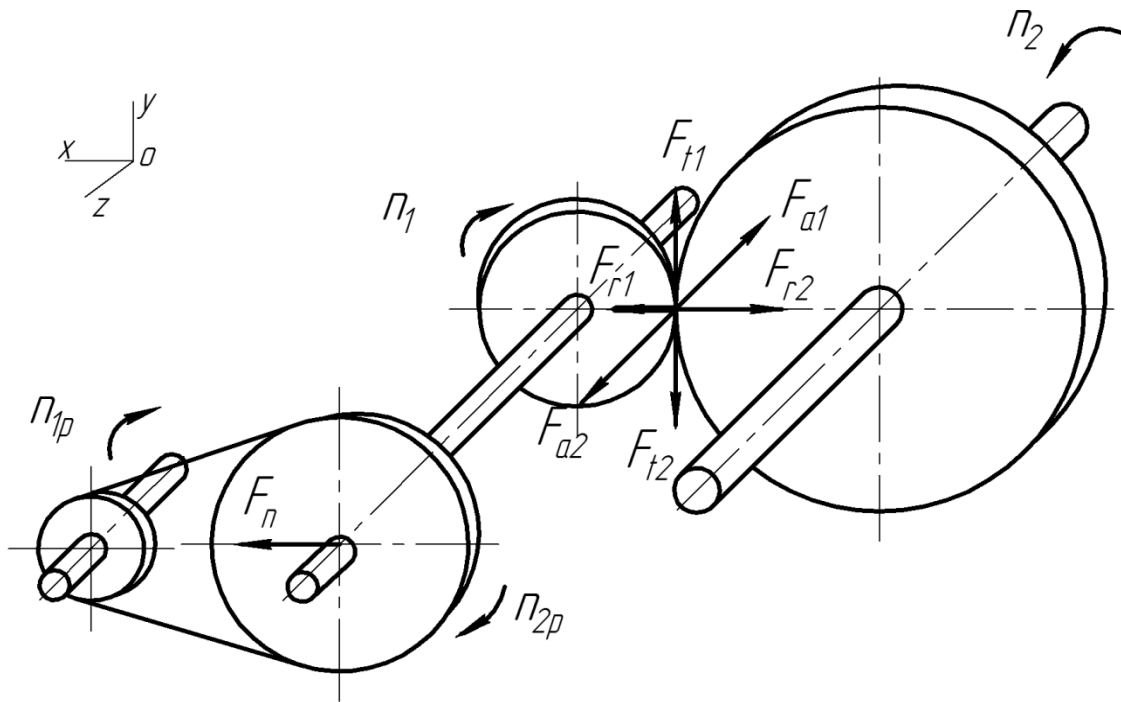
Редуктор цилиндрический одноступенчатый с ременной передачей
